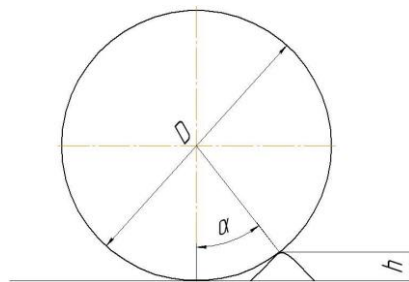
Розрахункова схема до визначення діаметра копіювального колеса
